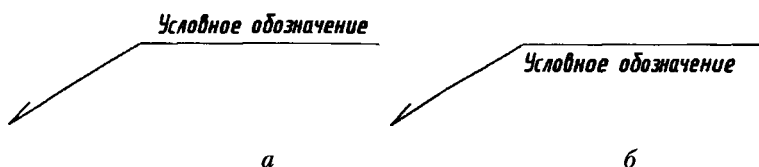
Условное обозначение видимого (а) и невидимого (б) сварного шва
